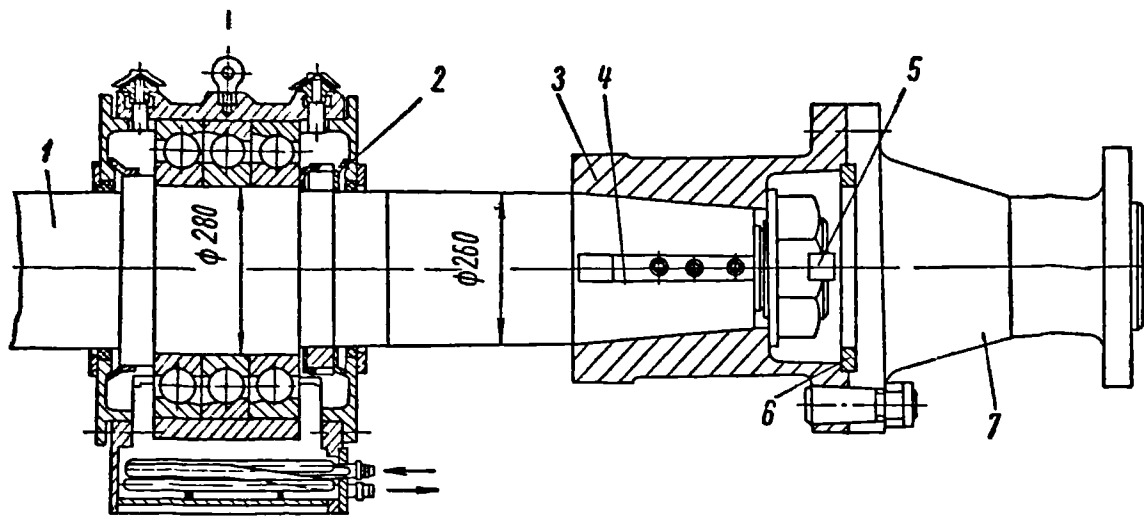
Общий вид упорного шарикоподшипника судового валопровода.
